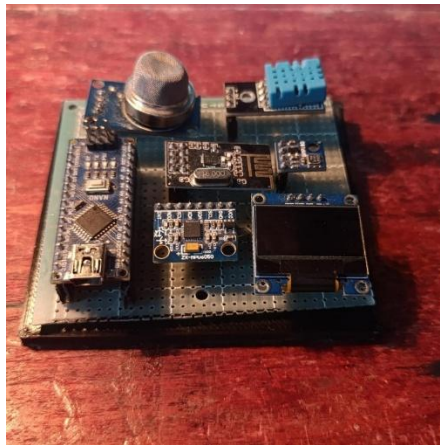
Prototipo de PCB casera en soporte de placa en3D
